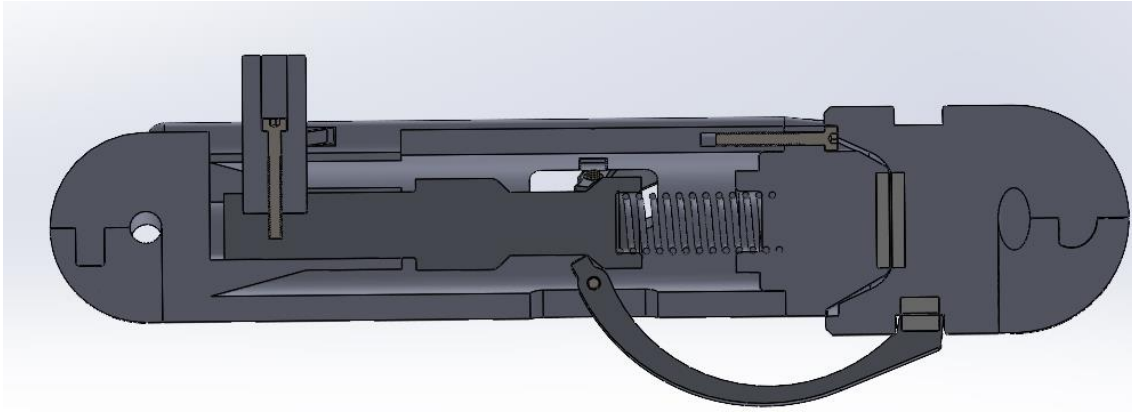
Vista seccionada del conjunto mosquetón en posición de cierre de garras sobre el subconjunto inferior.
